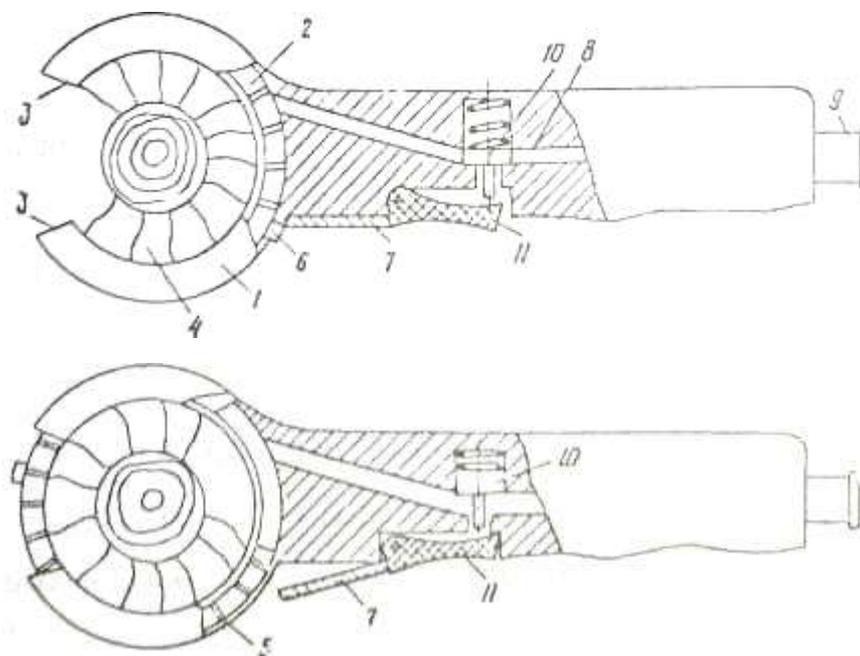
Схема приспособления пневматического типа для сбора ягод облепихи:
